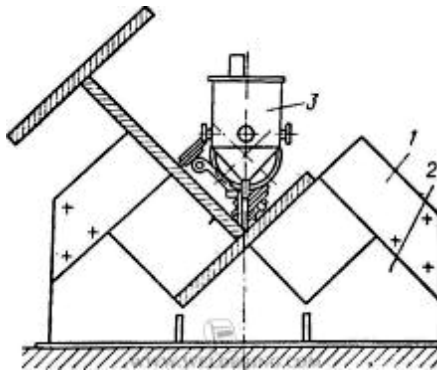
Схема универсального стенда для сварки балок:
